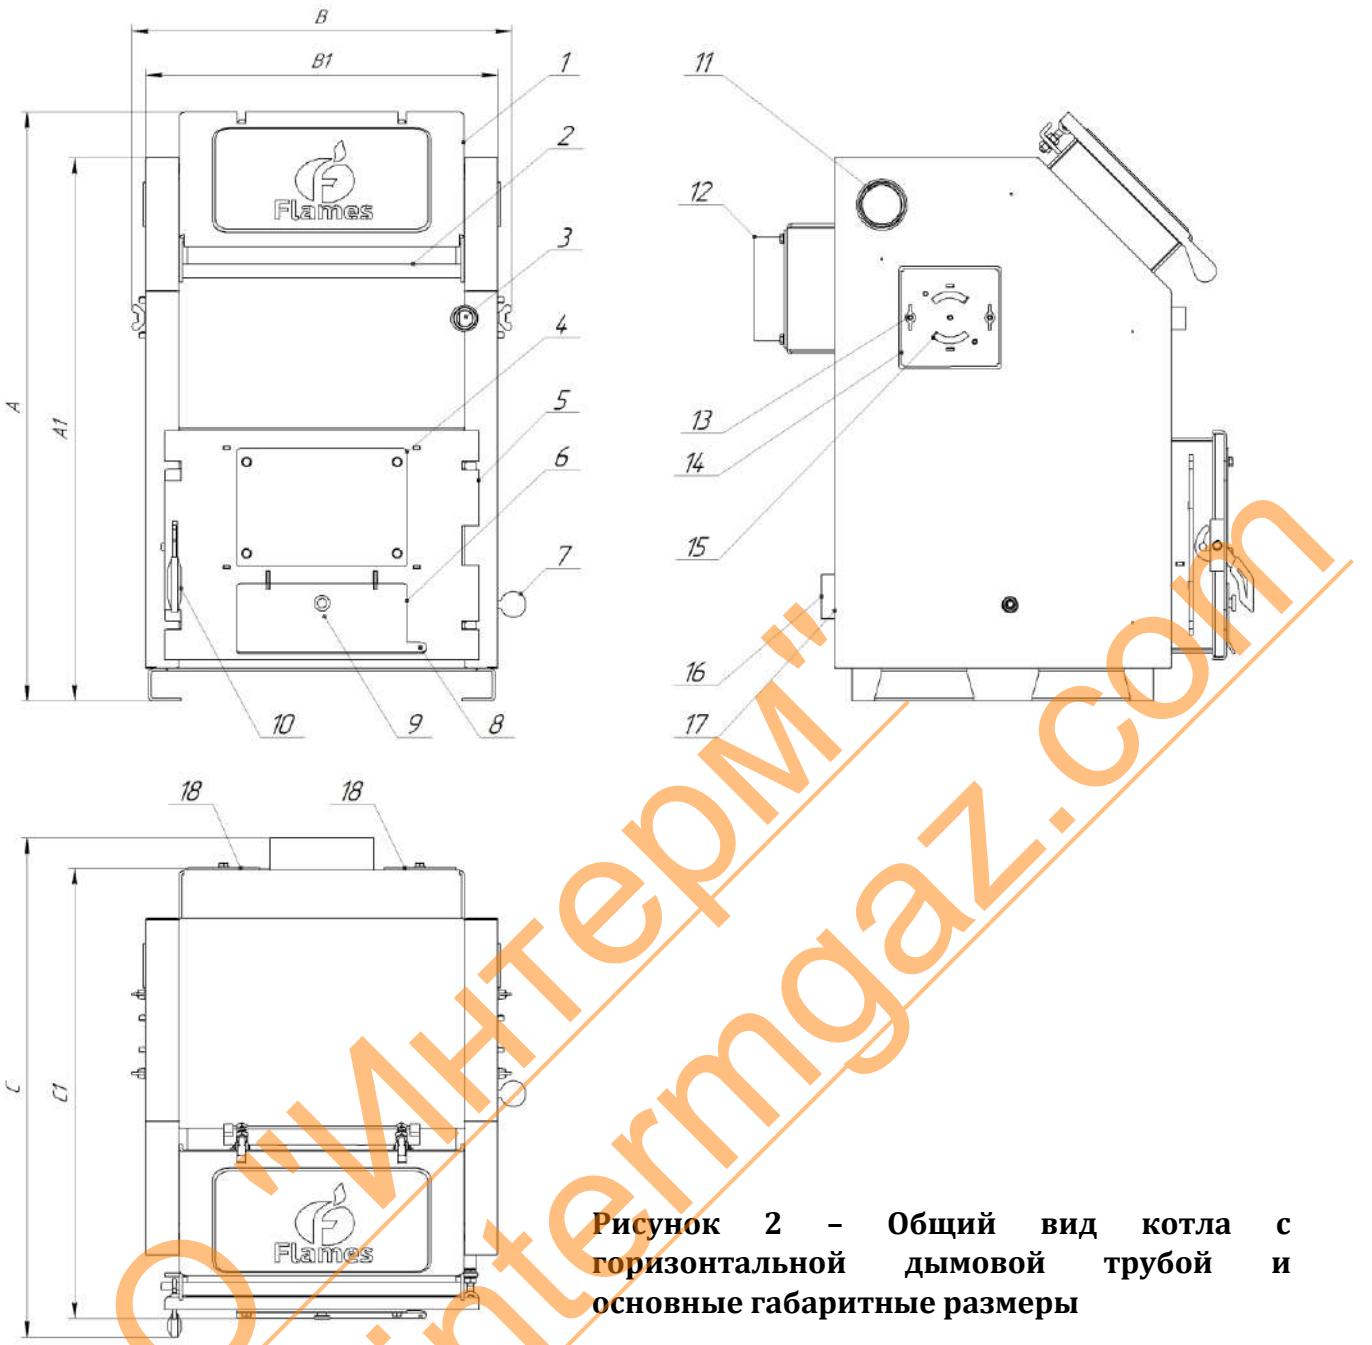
Общий вид котла с горизонтальной дымовой трубой и основные габаритные размеры
